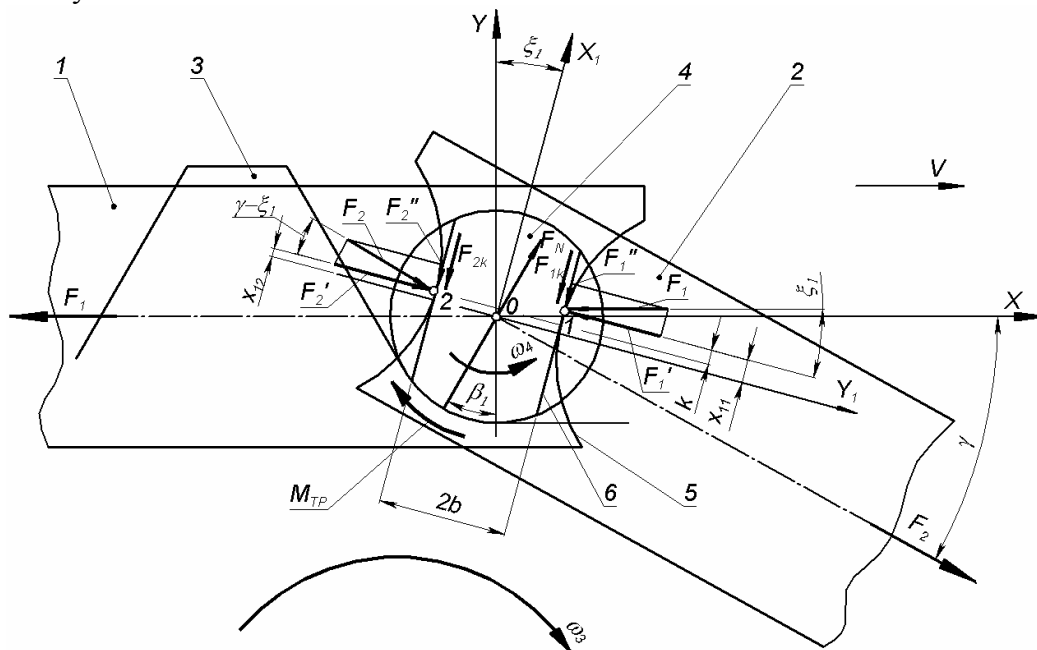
Схема сил, що діють на валик ланцюга з шарнірами тертя кочення: 1 і 2 – пластини ланцюга; 3 – зуб зірочки; 4 – валик ланцюга; 5 – опукла робоча поверхня отвору пластини; 6 – увігнута робоча поверхня валика
